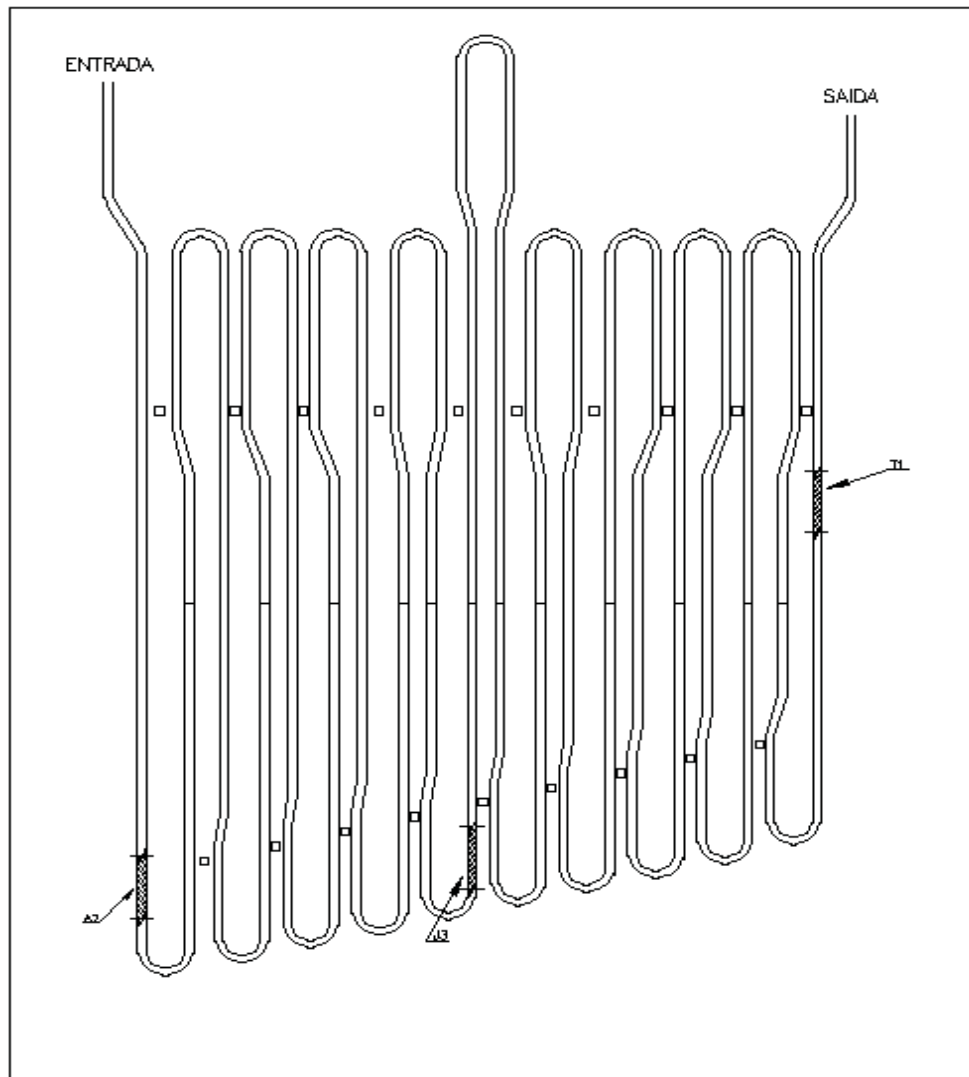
Croqui indicando a localização das amostras A2, J3 e T1.
